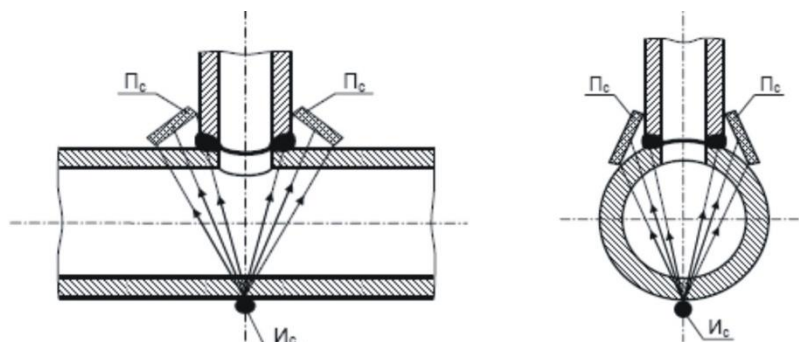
Схема просвечивания углового сварного соединения изнутри трубы за одну установку источника излучения
